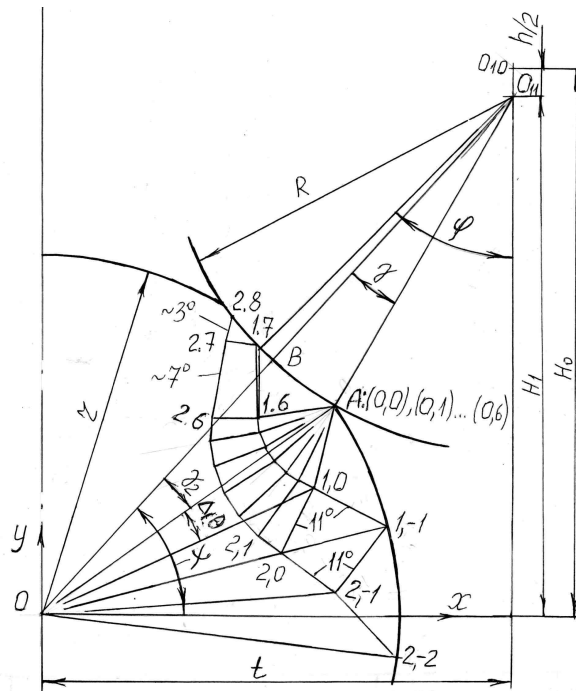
Поле линий скольжения при обжати круглой заготовки вырезными профилированными бойками
